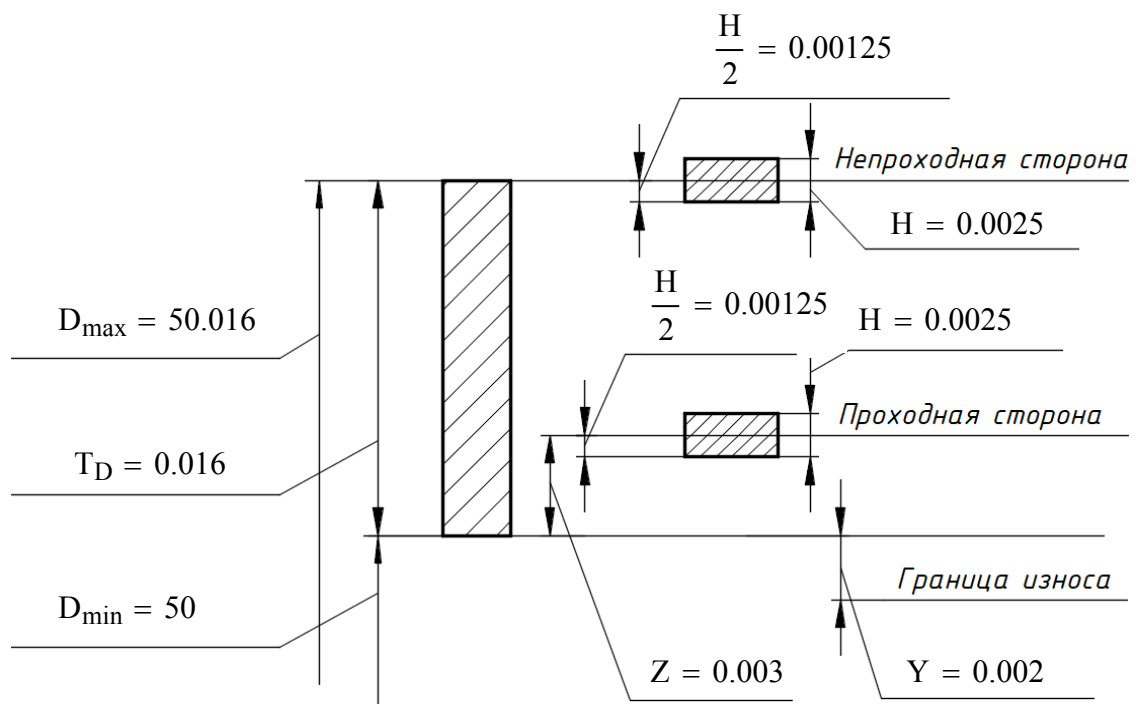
Схема расположения полей допусков калибра-пробки
